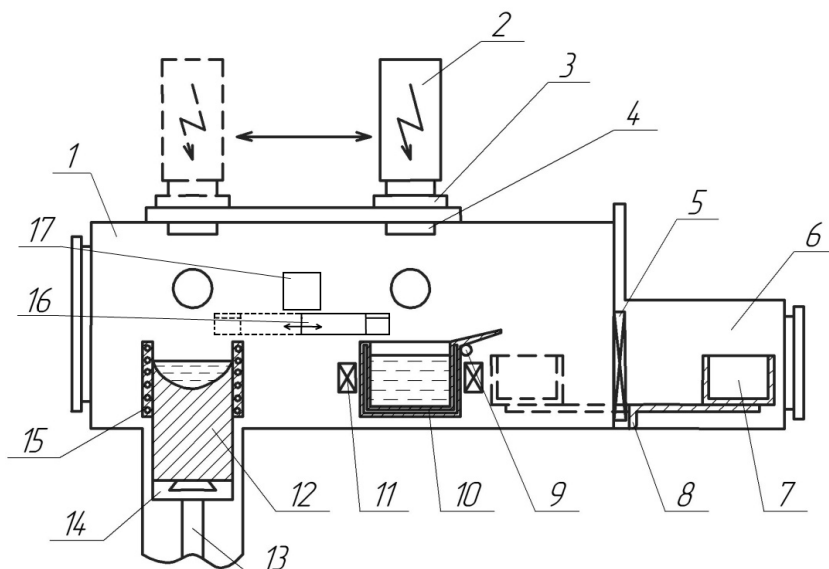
Схема электронно-лучевой установки для получения слитка и литой заготовки: 1 – плавильная камера, 2 – пушка ВТР, обогревающая тигель и кристаллизатор, 3 – подвижная плита, 4, 5 – вакуумные затворы, 6 – камера литейных форм, 7 – блок литейных форм, 8 – устройство перемещения форм, 9 – ось поворота тигля, 10 – тигель, 11 – система ЭМП тигля, 12 – слиток, 13 – механизм вытягивания слитка, 14 – поддон, 15 – кристаллизатор, 16 – промежуточная ёмкость, 17 – устройство подачи шихты
